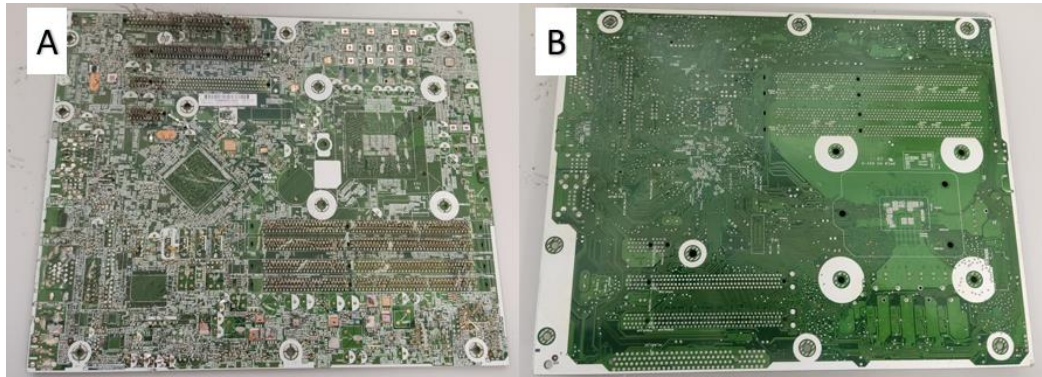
Parte delantera (A) y trasera (B) de PCB de ordenador sin aparatos electrónicos, lavada y seca.
